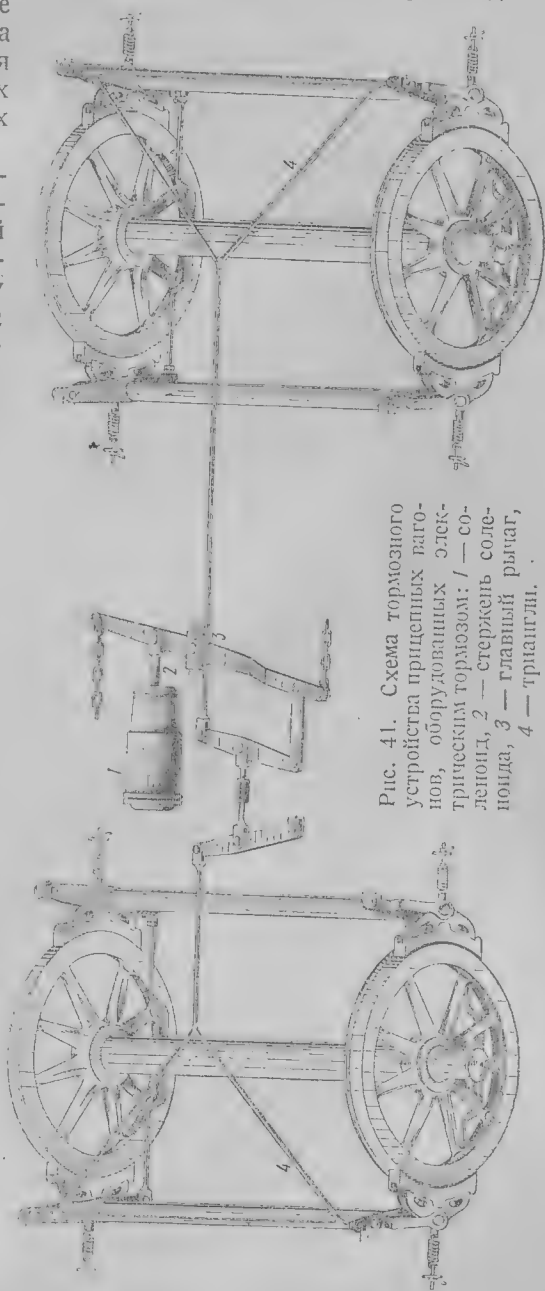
Схема тормозного устройства прицепных вагонов, оборудованных электрическим тормозом: 1 — соединенд, 2 — стержень соединенд, 3 — главный рычаг, 4 — траверза.
